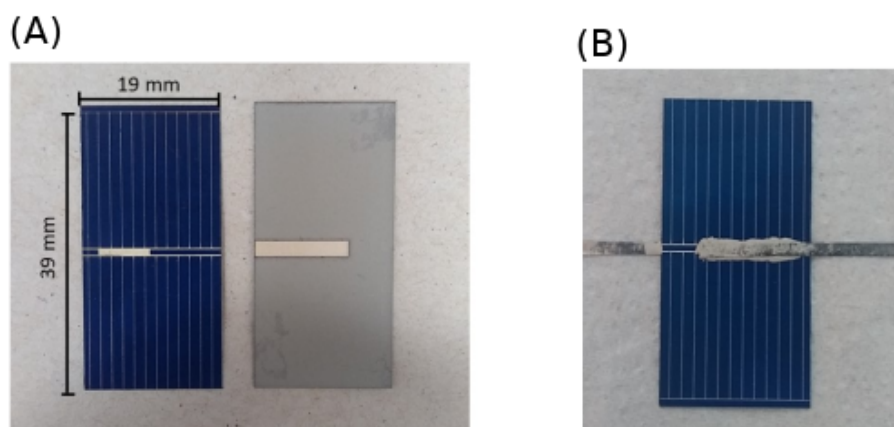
Painel solar antes e depois da soldagem dos contatos elétricos: (A) antes da soldagem, imagem da parte superior e inferior do painel; (B) após a soldagem.
